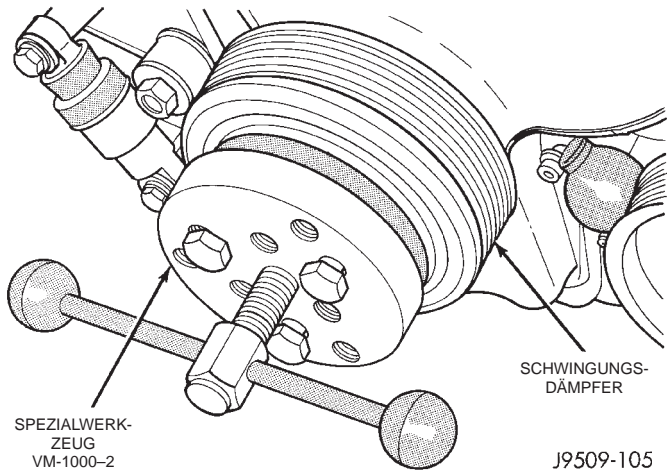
Ausbau des Schwingungsdämpfers mit Spezialwerkzeug VM-1000-2
